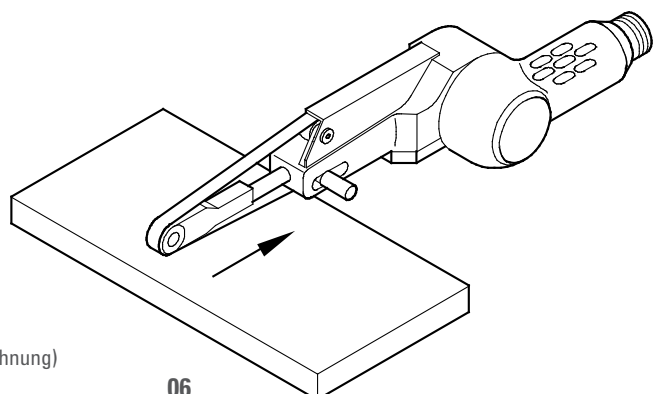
Flächen bearbeiten (Symbolzeichnung)
